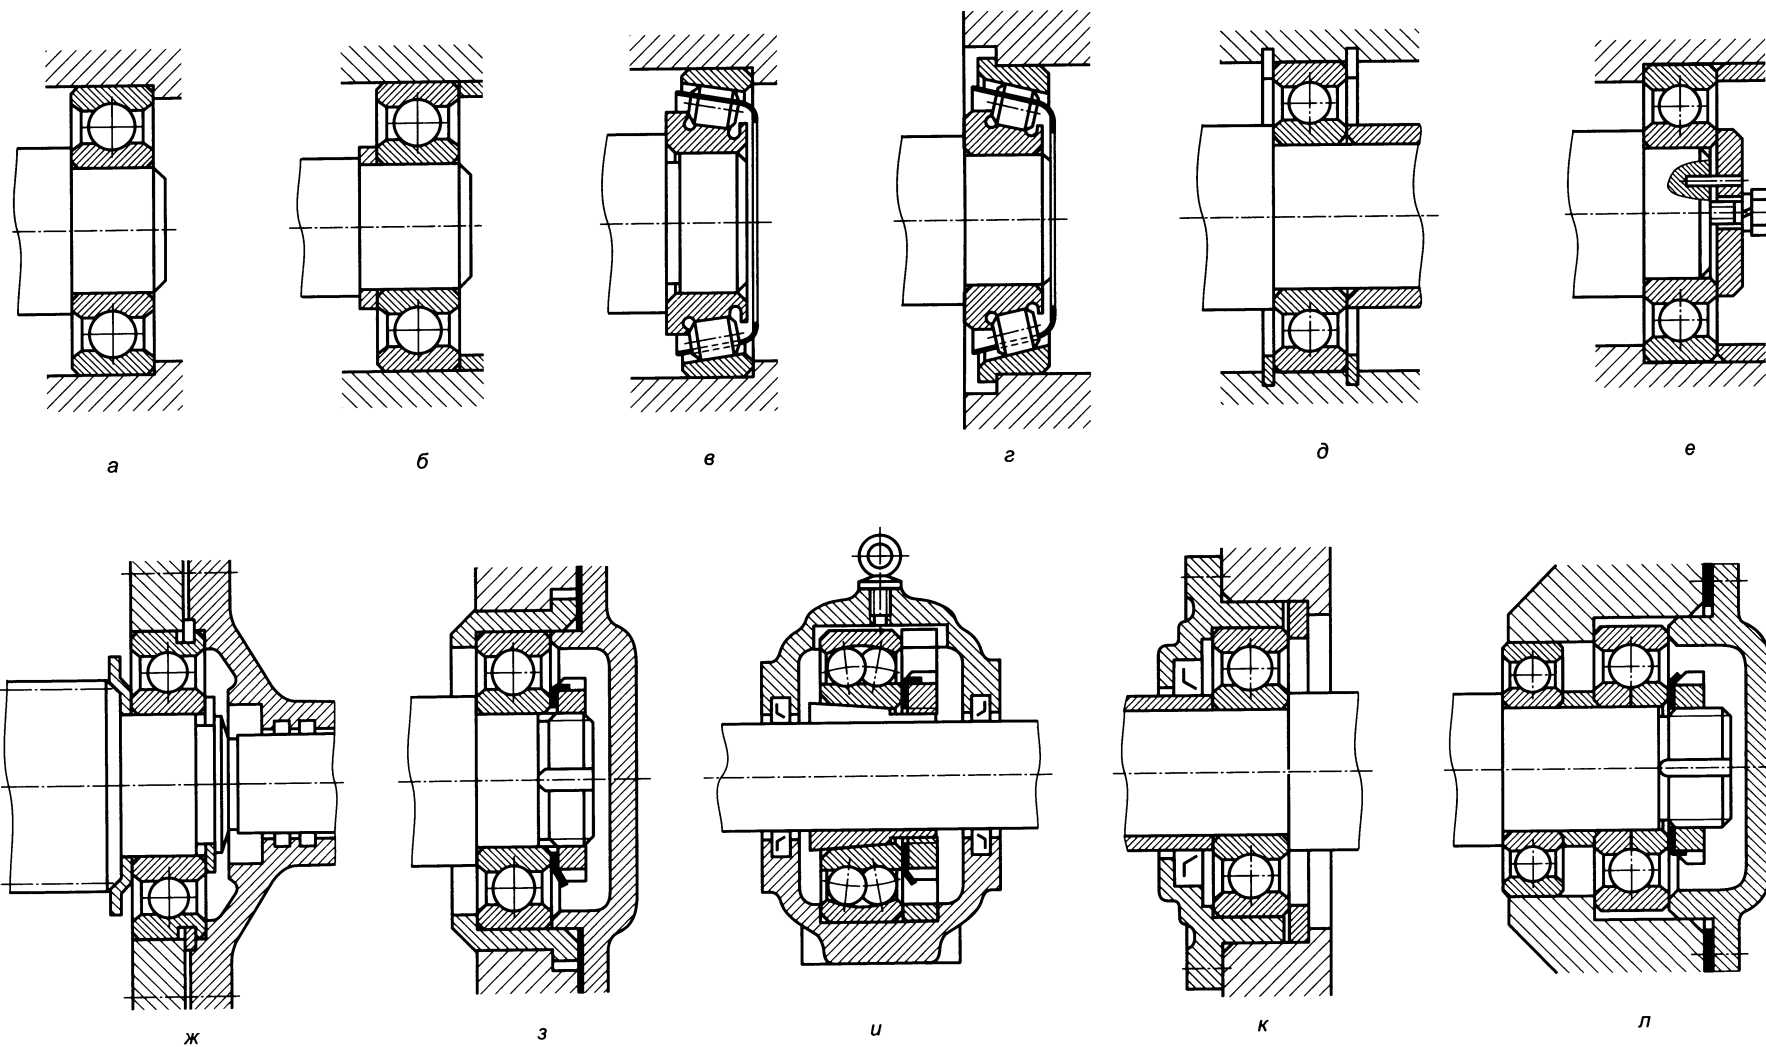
Примеры закрепления подшипников на валу, осях и в корпусе
